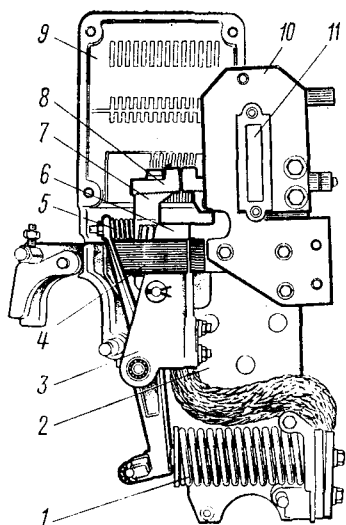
Контактный элемент с дугогашением контроллера ЭКГ-8
